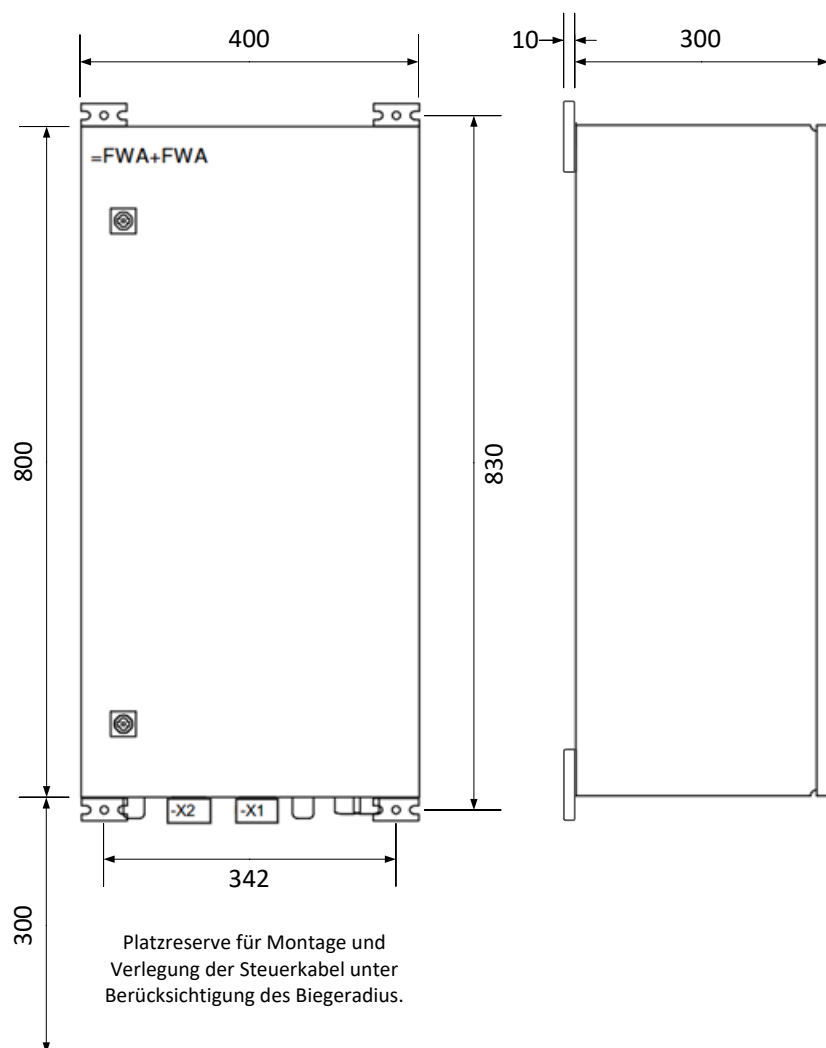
Maße und Befestigung Fernwirkschrank
